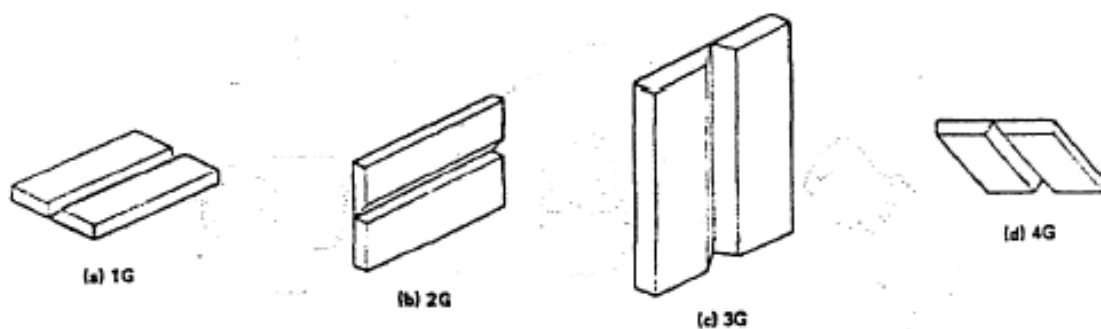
POSICIONES DE SOLDADURA EN PLACAS CON SOLDADURA DE RANURA. (Ref. 5)
